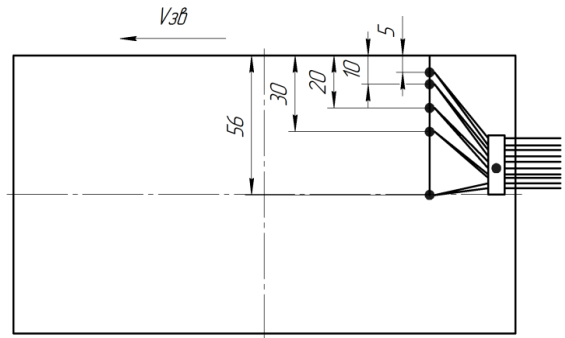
Схема розташування хромель-копелевих термопар, приварених на робочу поверхню штампа
